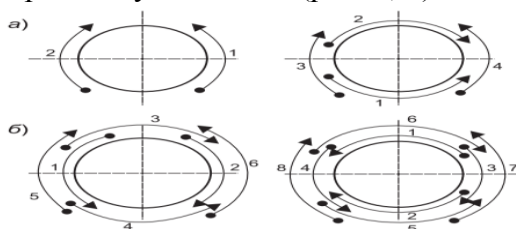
Схема сварки стыка трубы: а - второго слоя; б - третьего слоя
